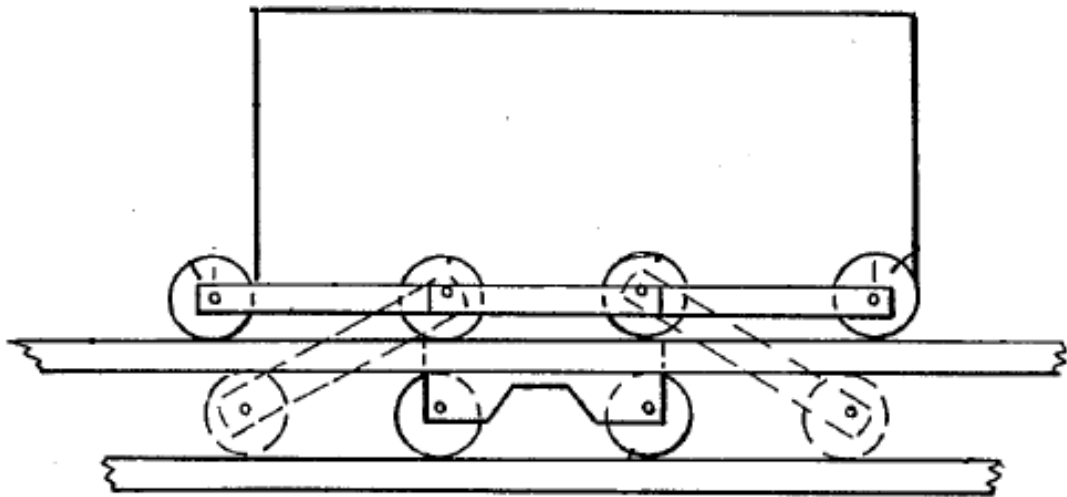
Схема несучих пластин пластинчатого транспортеру
